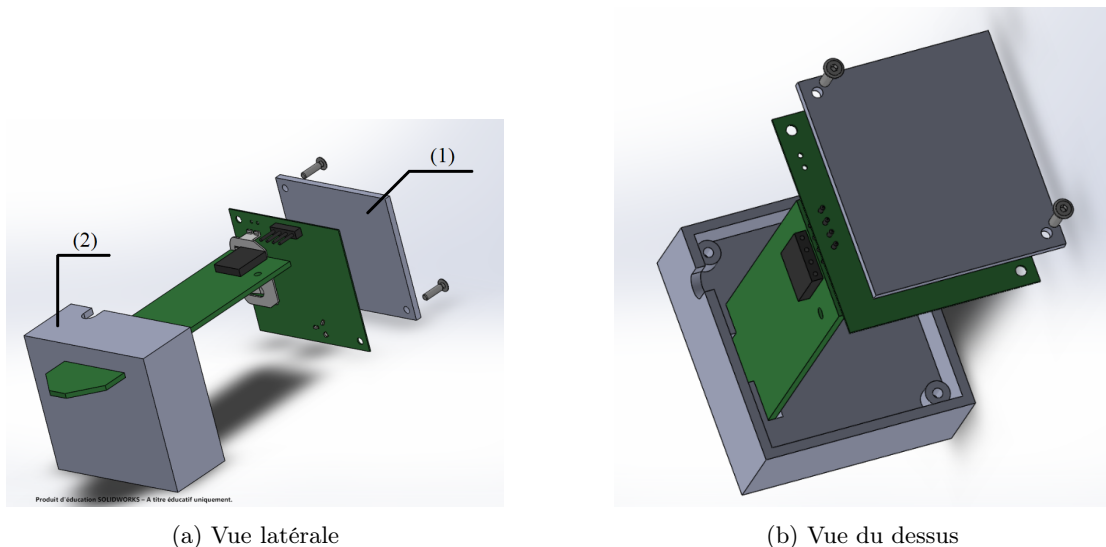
Vues 3D de l’assemblage du boîtier sur le PCB
